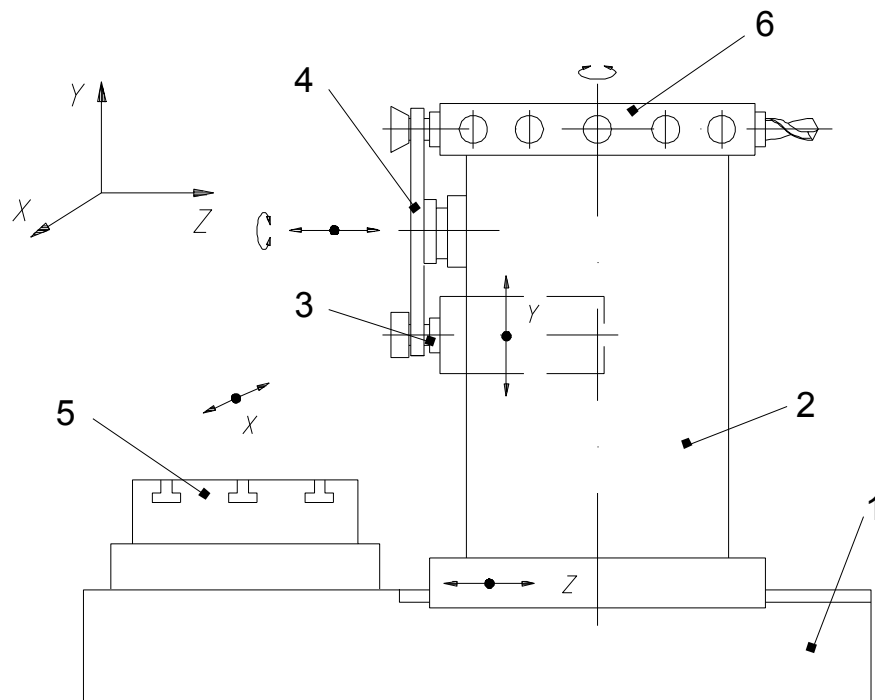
Компоновка багатоцільового верстату з верхнім розміщенням інструментального магазину
